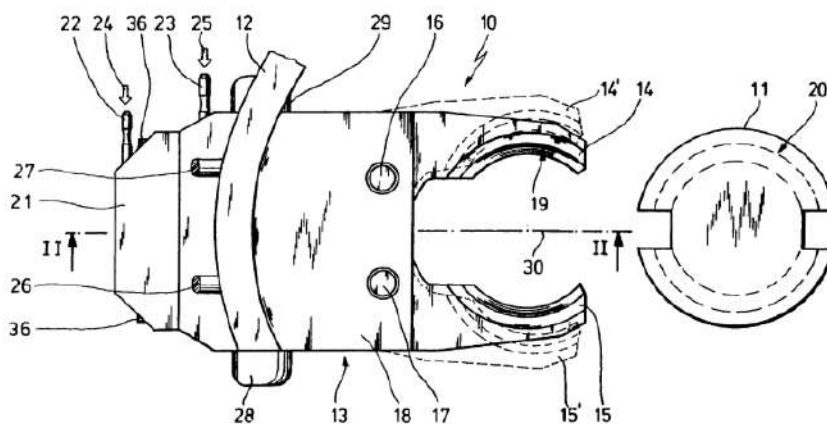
Vista superior del Gripper para el intercambio de herramientas en disposición cerrada.
